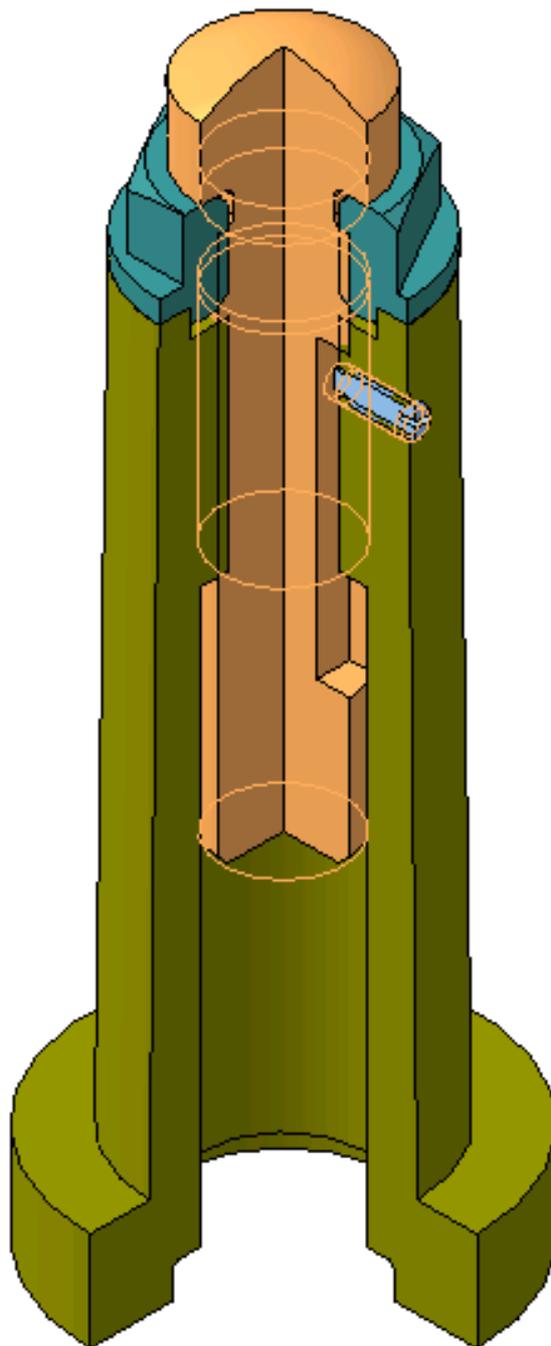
3D-модель сборки изделия «Подпорка винтовая»
